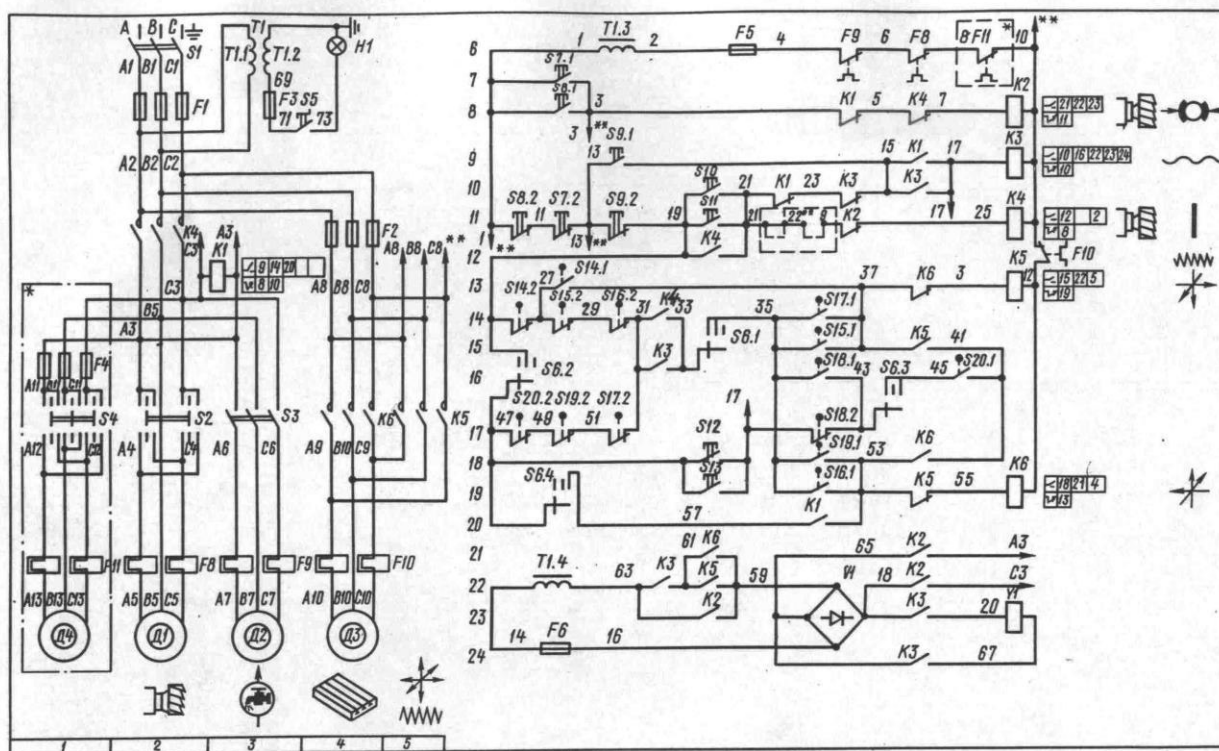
Схема наладки электрооборудования фрезерного станка
